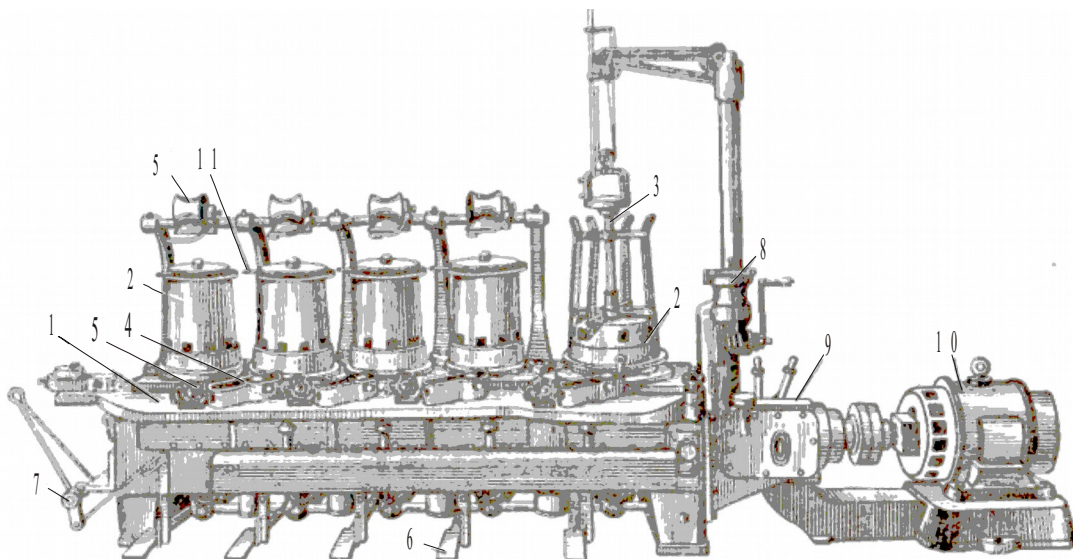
Машина 5/350 багаторазового волочіння: 1 - станина; 2 - барабан; 3 - знімач; 4 - мильниця з волоку тримачем; 5 - напрямні ролики; 6 - педаль включення й вимикання; 7 - відмикач при заплутуванні мотка; 8 - знімний пристрій; 9 - коробка швидкостей; 10 - двигун; 11- повідковий пристрій
